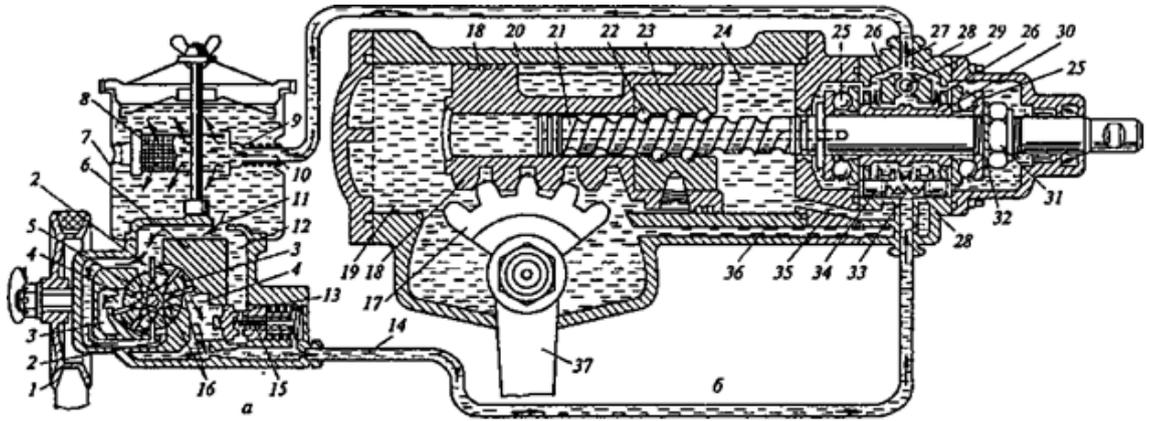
Рулевой механизм и усилитель ЗИЛ-4314
